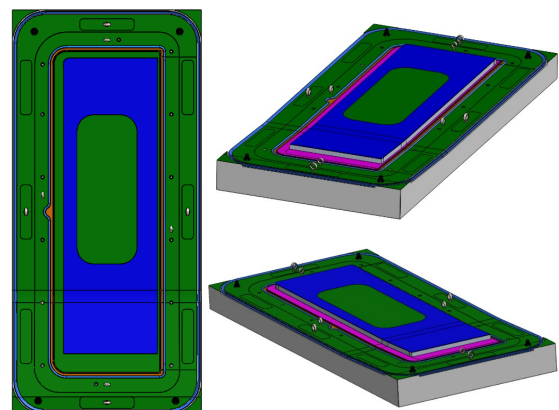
Diseño del molde modular para la fabricación de las puertas izquierda y derecha
